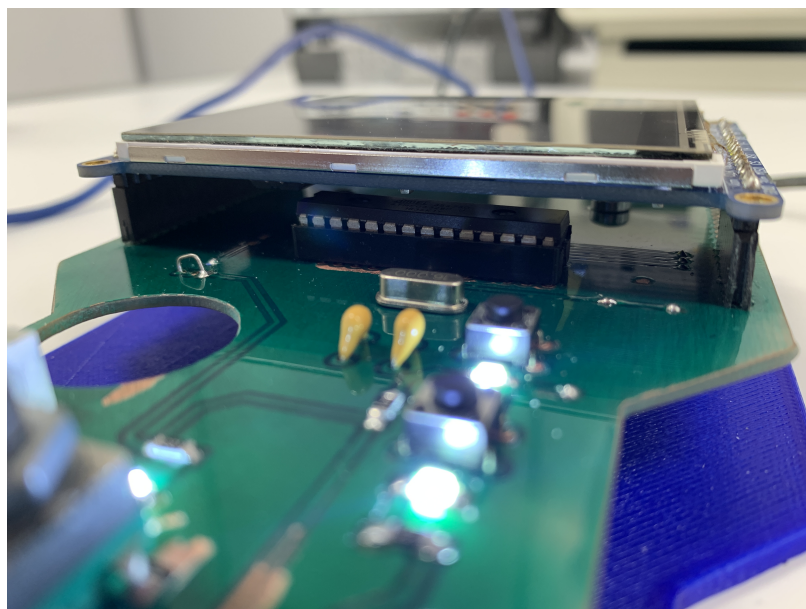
Vista del ATmega328P montado sobre la PCB debajo de la pantalla.
